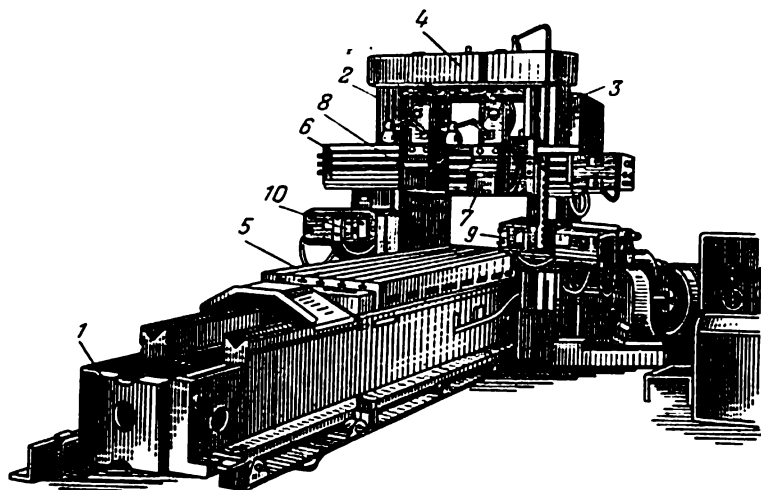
Vue d'ensemble d'une raboteuse modèle 7231A
